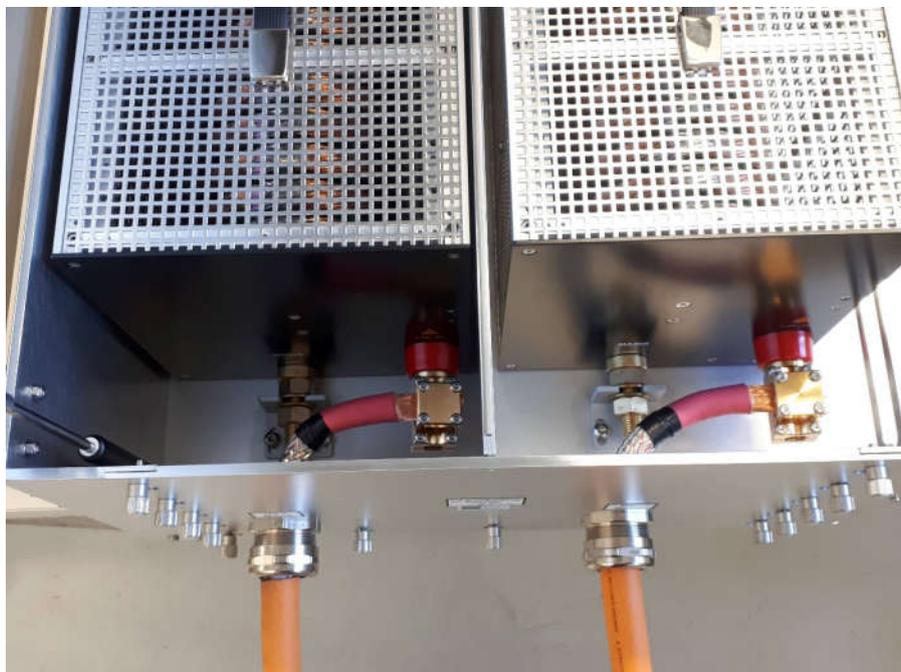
Flanschplatte mit HV-Kabeln und Klemmen in montiertem Zustand
